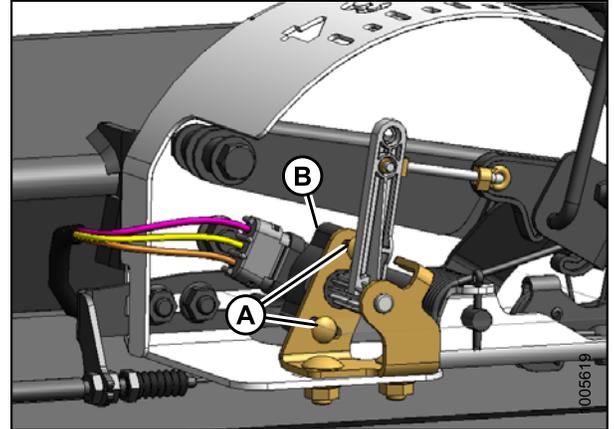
Ensemble de capteur de hauteur automatique de plateforme pour moissonneuses-batteuses autres que Lexion
